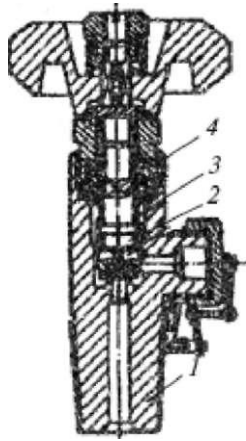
Вентиль для пропан-бутана: 1 - корпус; 2 - клапан; 3 - резиновый манжет; 4 - шпindelь
